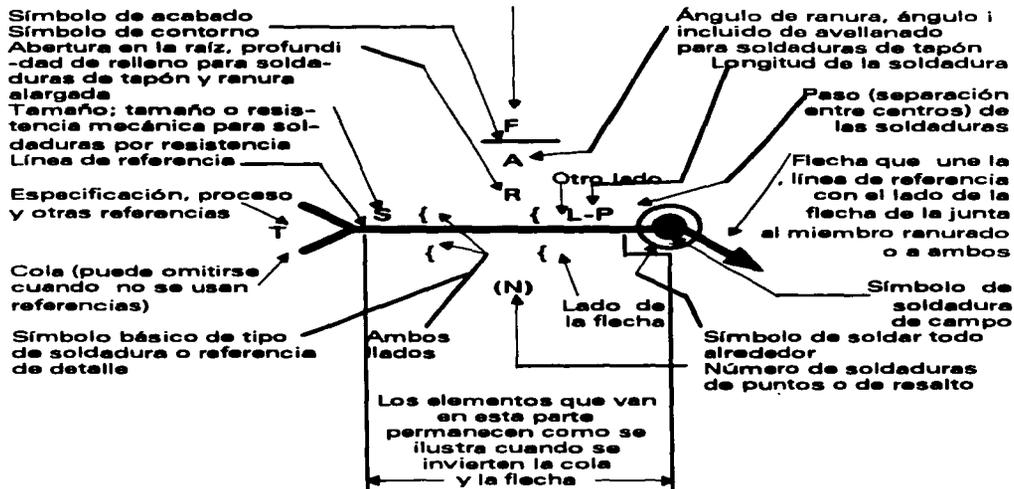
SÍMBOLO COMPLETO DE SOLDADURA^{REF.}
